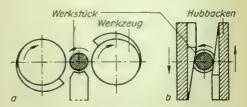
Querwalzen mit keilförmigen Werkzeugen: a umlaufende, b auf- und abgehende Werkzeuge
